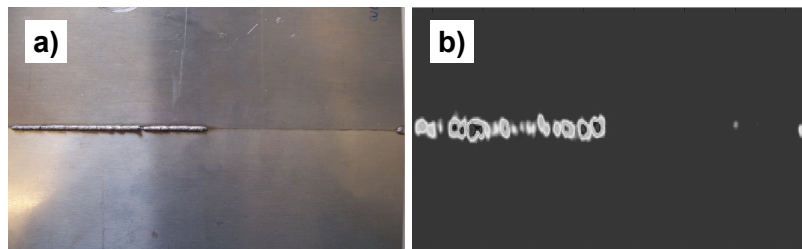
Foto (a) und NACE-Scan (b) einer Stahlprobe mit unvollständiger Schweißnaht [121].
